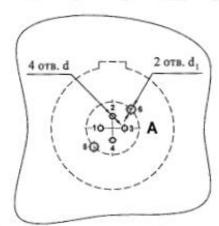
Схема расположения отверстий для установки соединителя СКЦ102-1/9 и СКЦ102-1/11... печатного монтажа
